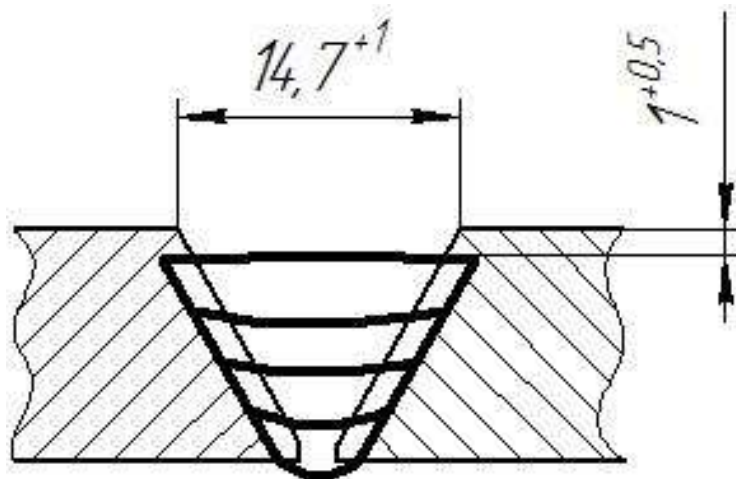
Выполнение заполняющего слоя сварного шва
